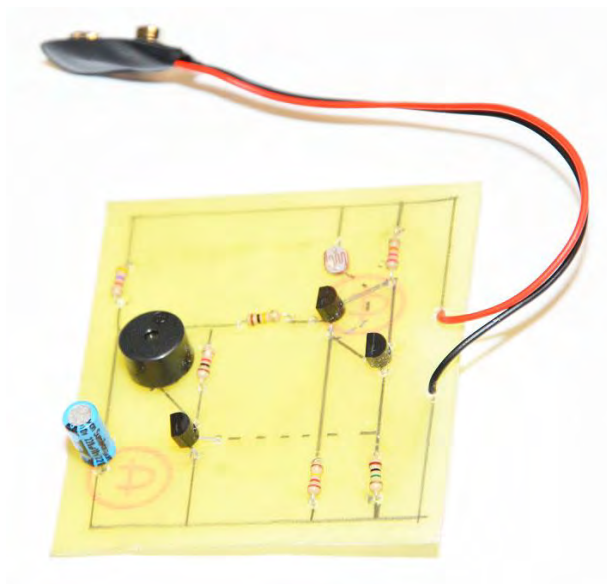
Zamontowane tranzystory T1 i T2 – widok od strony elementów
